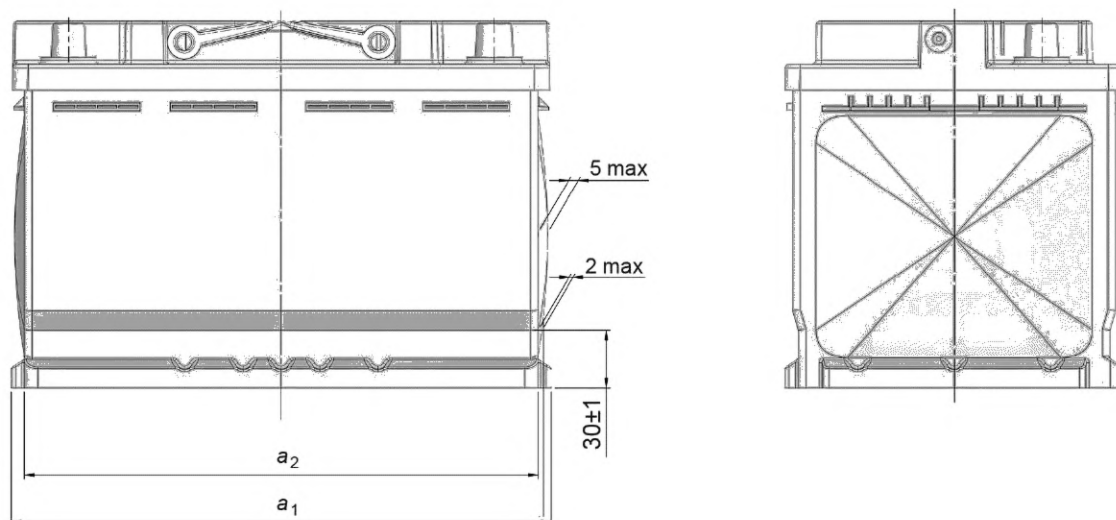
Размеры допустимой выпуклости боковых стенок корпуса на коротких сторонах батареи
